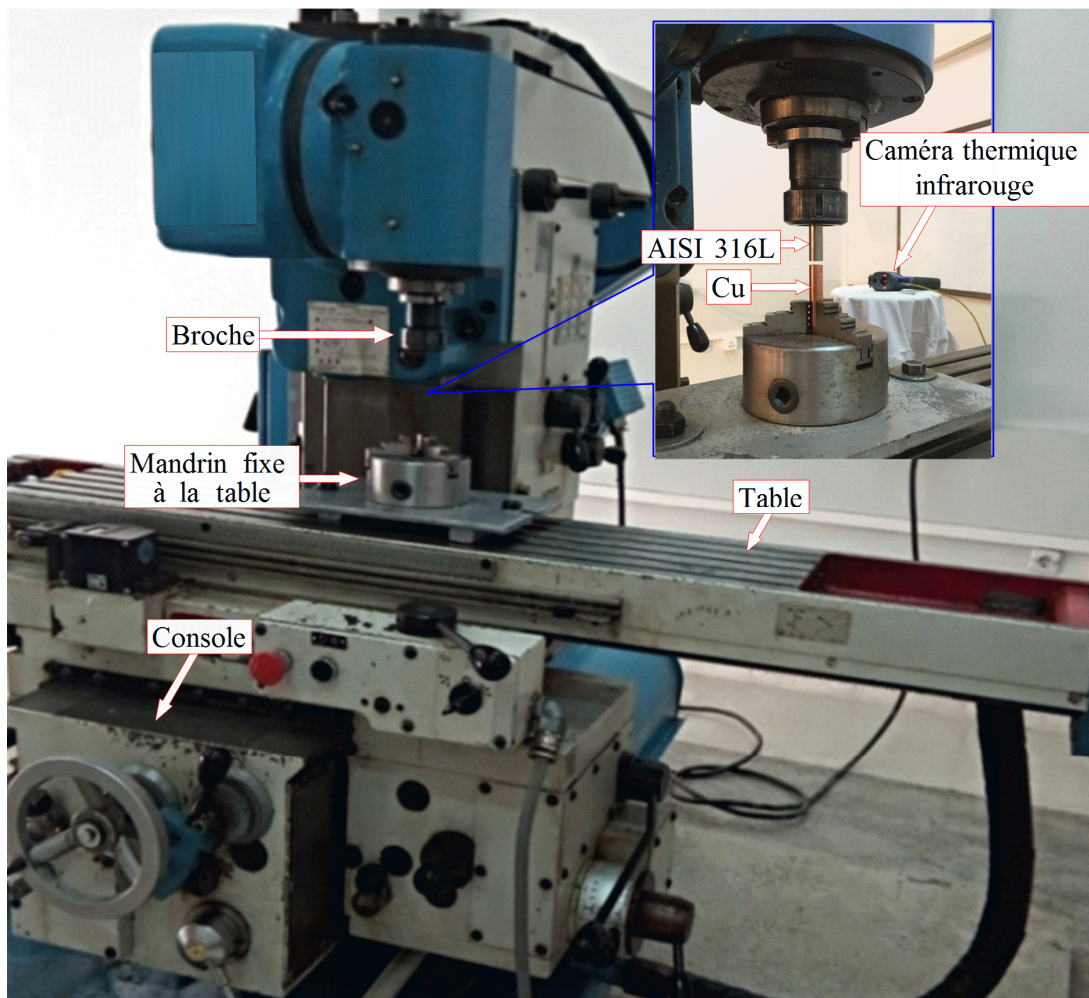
Procédé de soudage par friction rotative acier inoxydable AISI 316L – Cuivre
